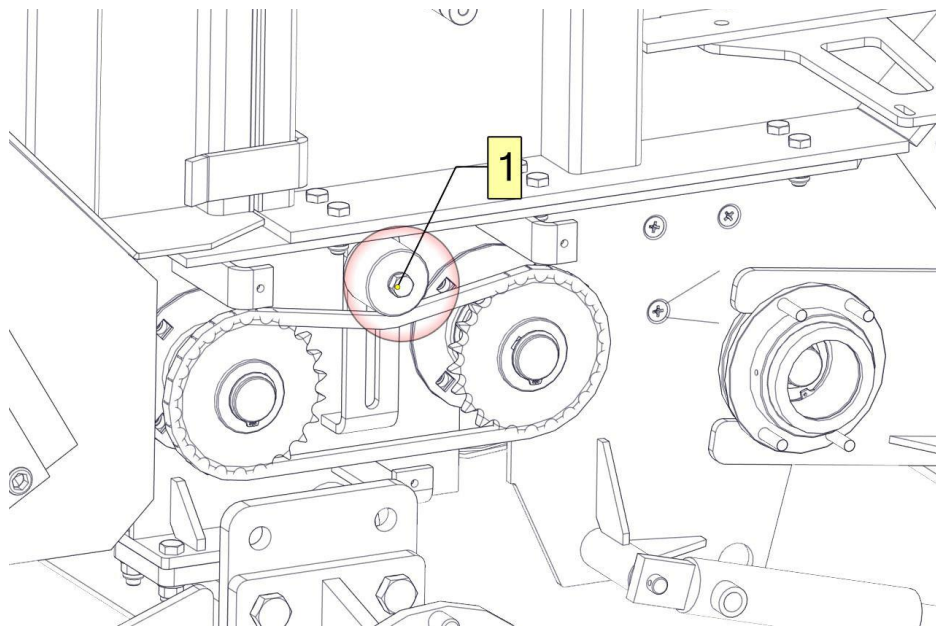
Регулировка натяжения цепи подборщика с правой стороны пресс-подборщика
